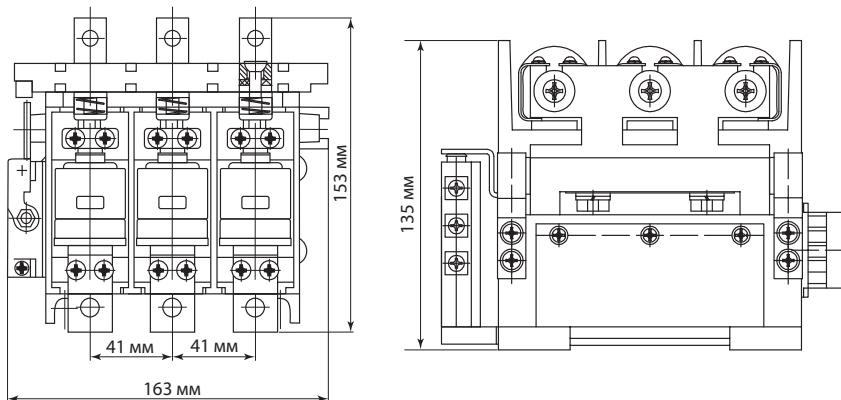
Габаритные размеры КВТ-1,14-80/125/160
